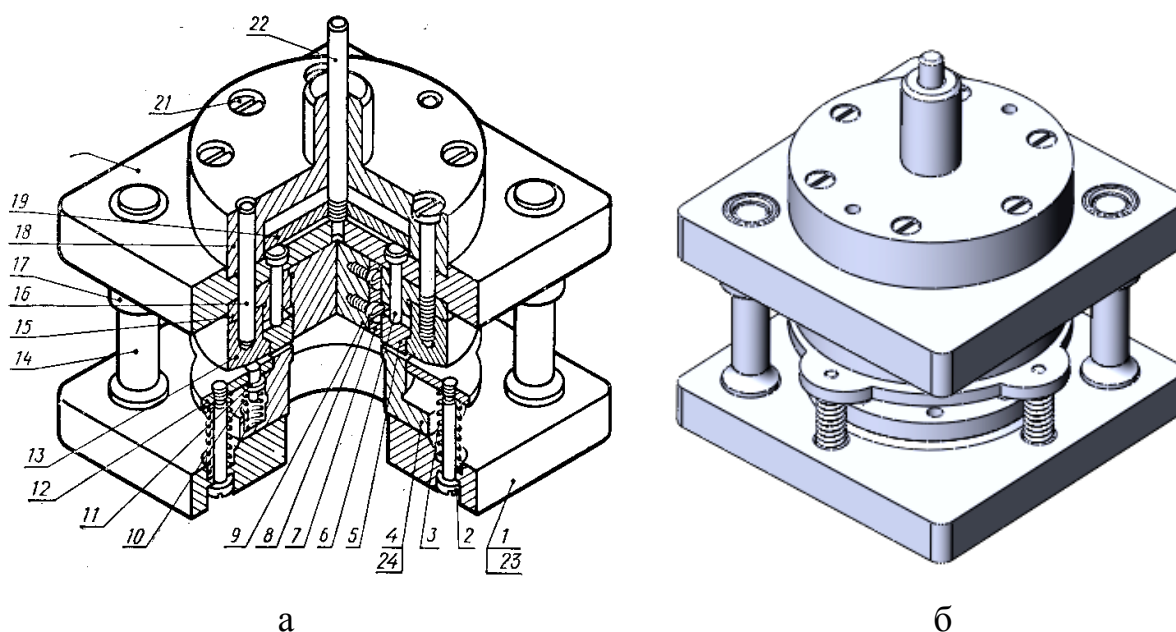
Штмп для виготовлення пластин ротора: а – креслення, б – 3D-модель
